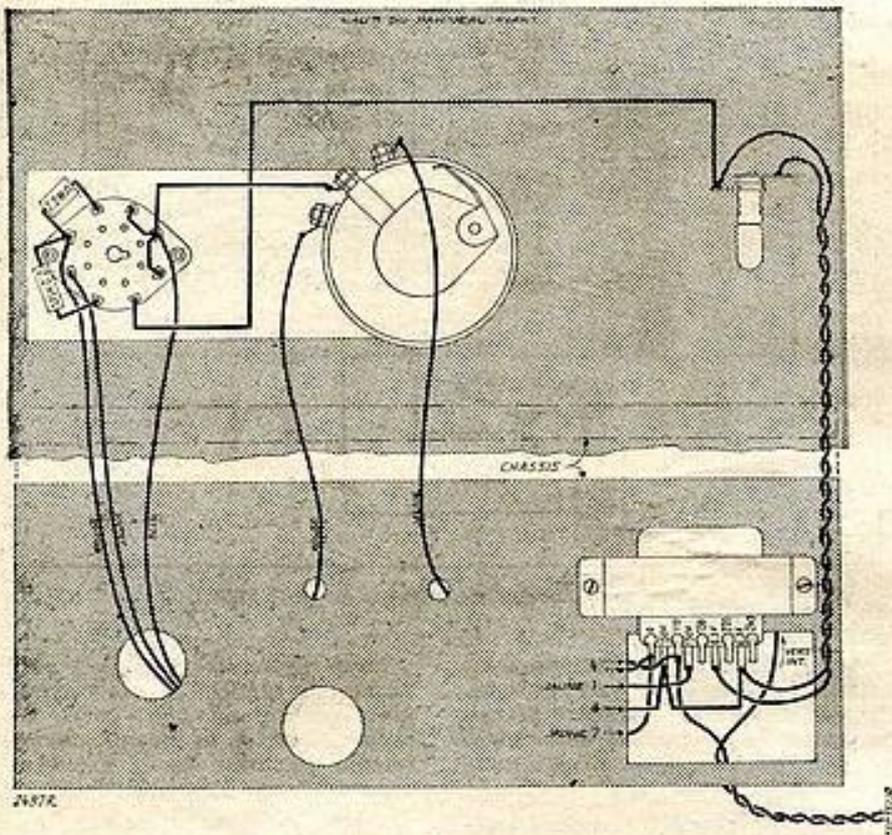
Vue du dessus du châssis et de l'arrière du panneau avant.
